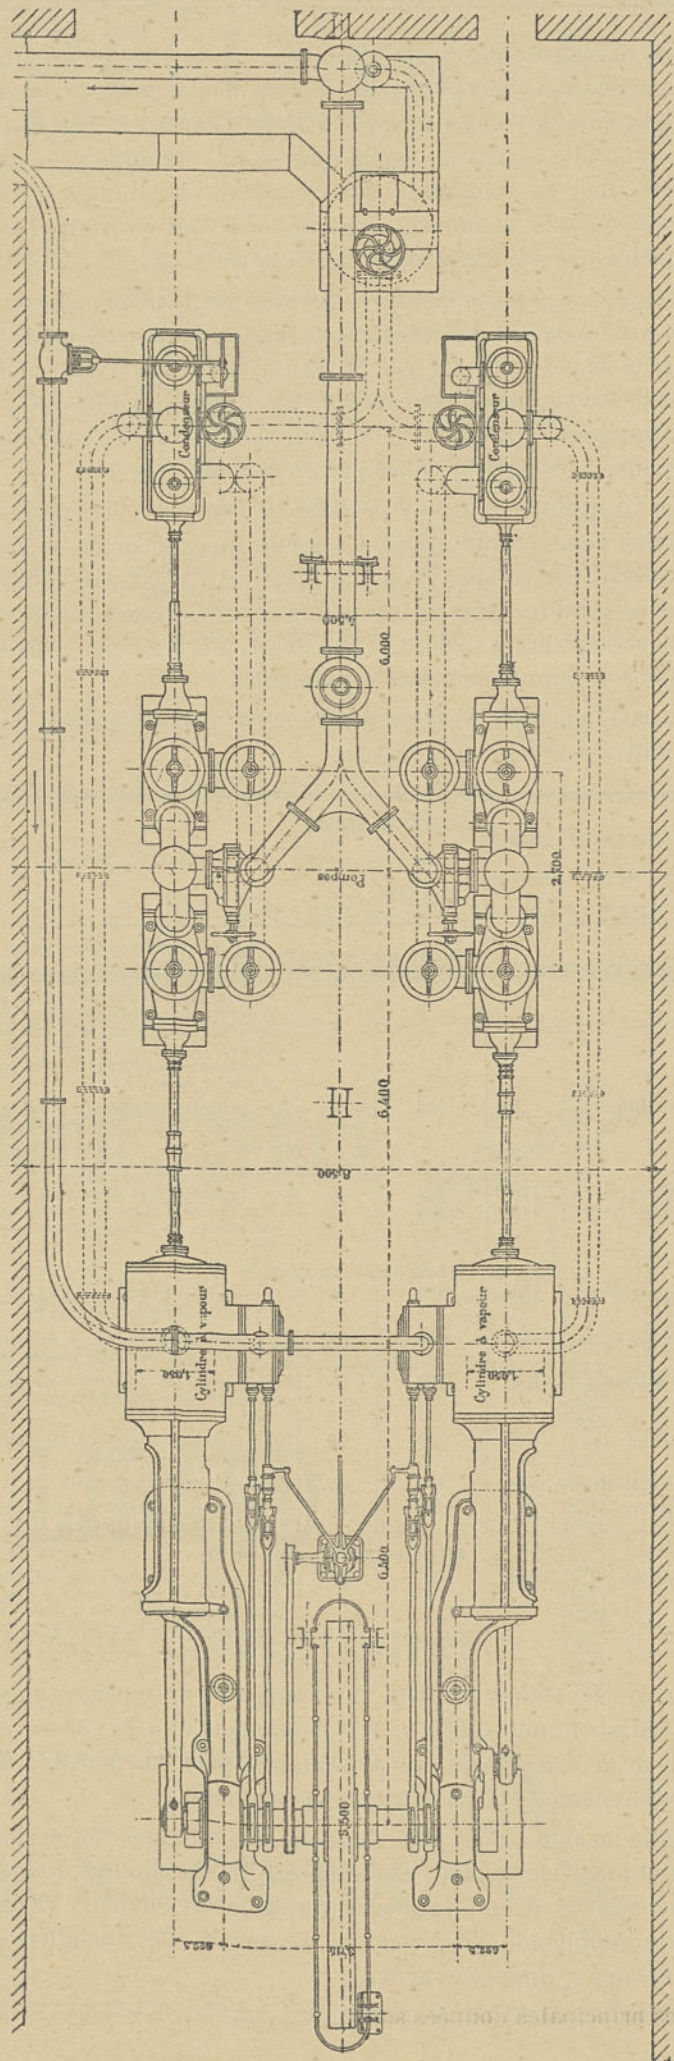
Pompe d'épuisement souterraine, de MM. Mailliet et C^e, d'Anzin. Plan.
